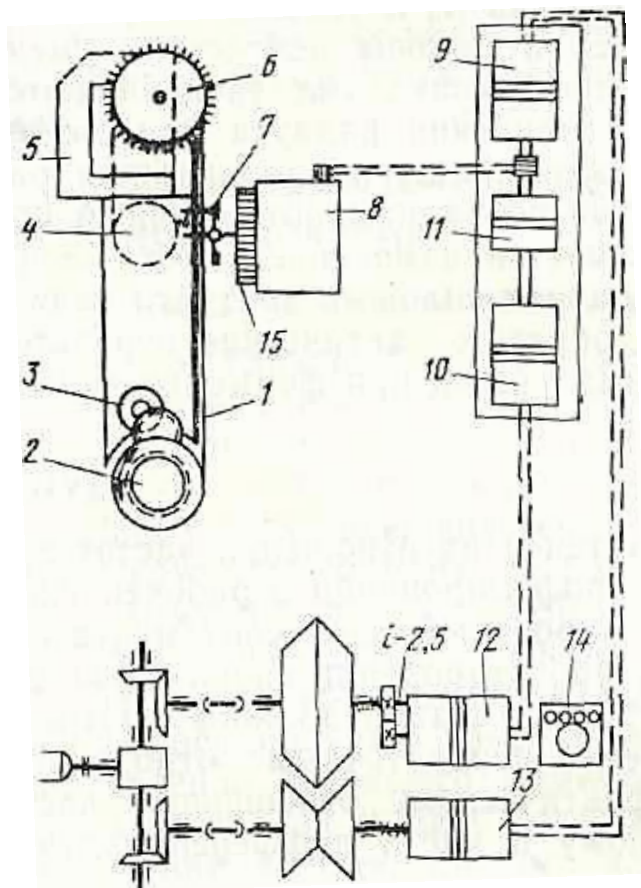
Схема измерительной установки для определения отношения чисел оборотов валка
